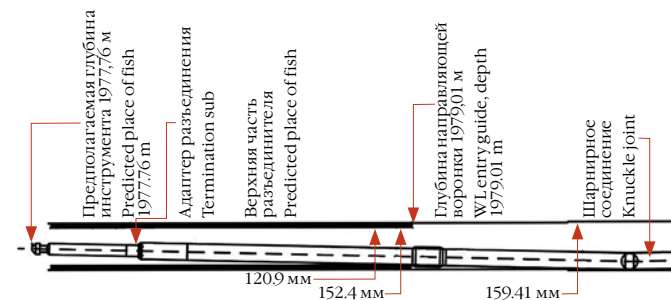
Схема аварийного инструмента с двумя различными ловильными шейками на скважине № 4
